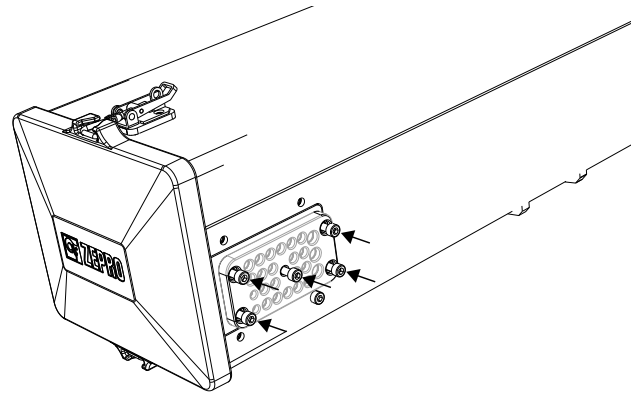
Fünf Schrauben der Kabeldurchführung
